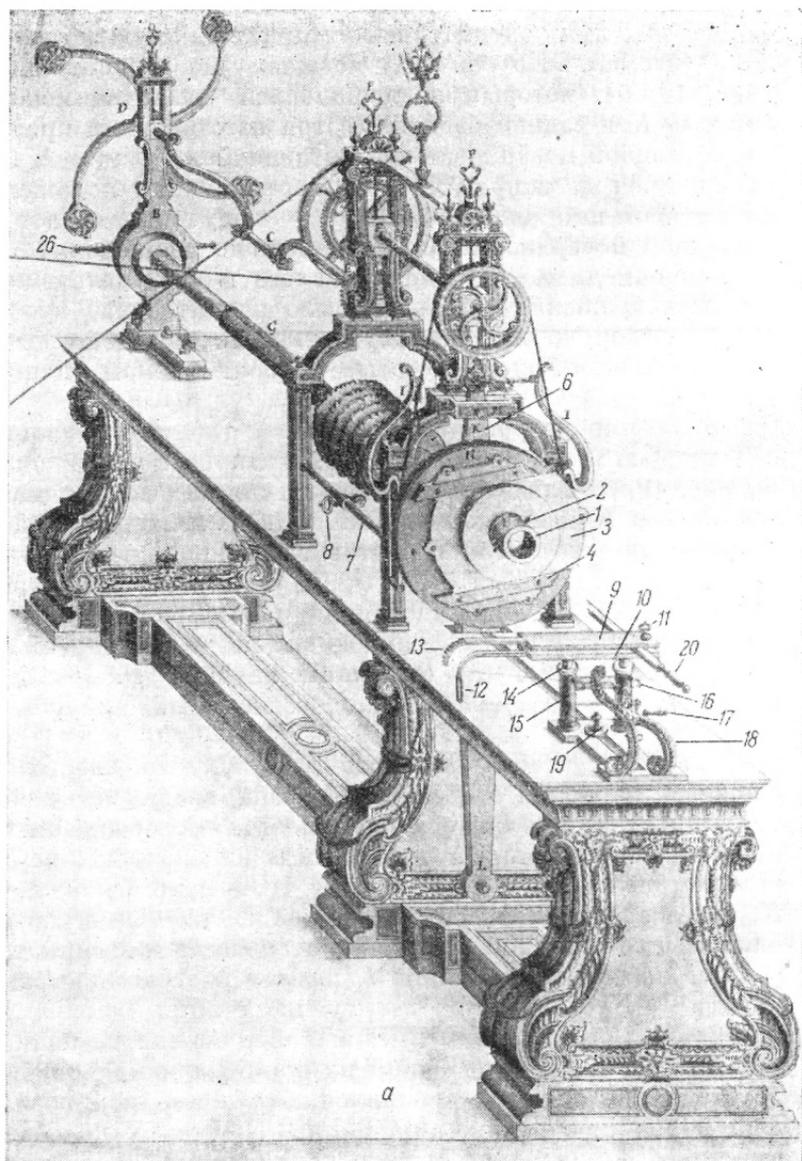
Токарно-овальерный станок («Театрум махинарум»).
